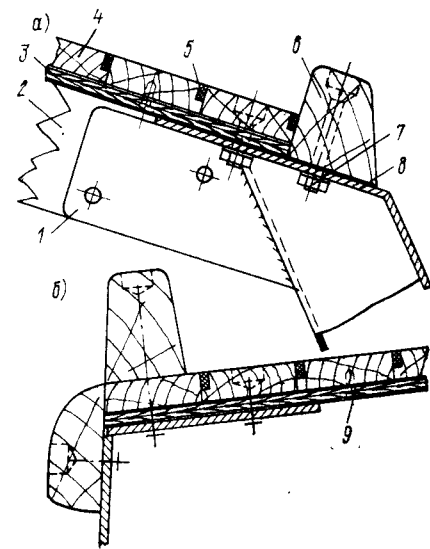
Два варианта соединения деревянной палубы с металлическим корпусом: а — для яхты «Секура» с надстройкой-баком; б — для гладкопалубной яхты.
